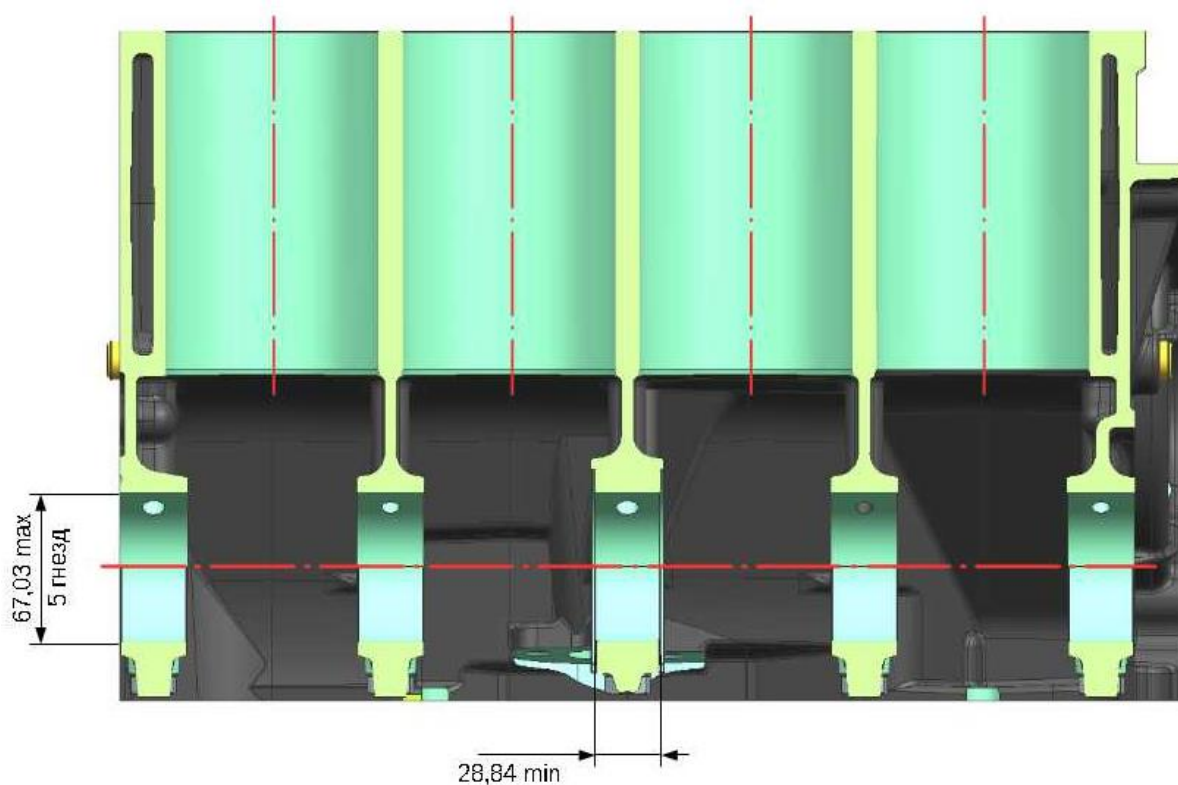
Предельные размеры гнезд коренных подшипников блока цилиндров
